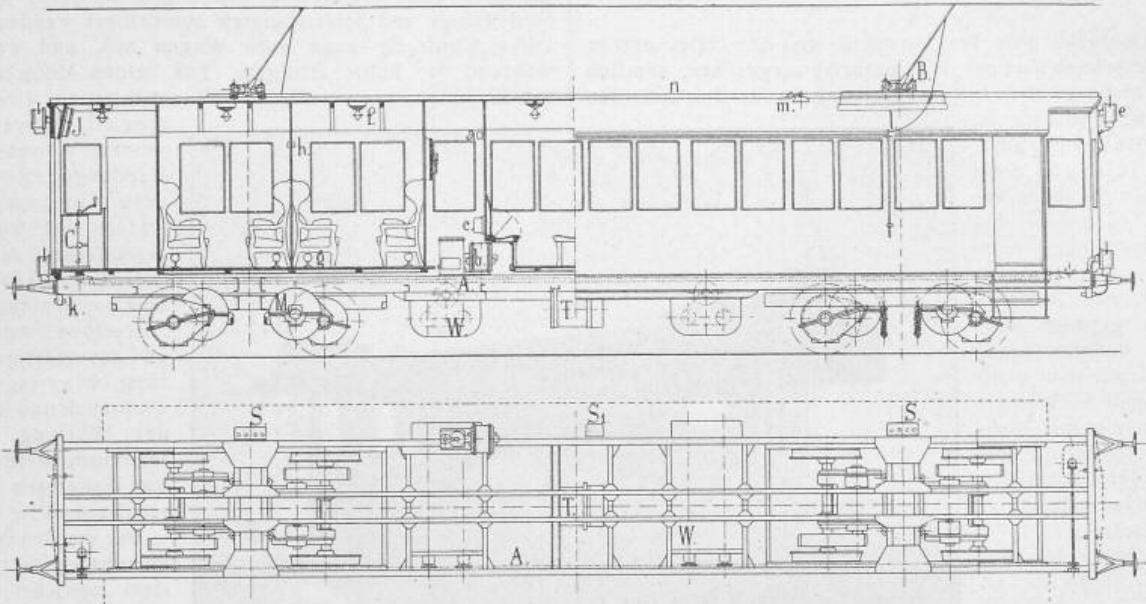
Ansicht und Grundriss. 1:100.
